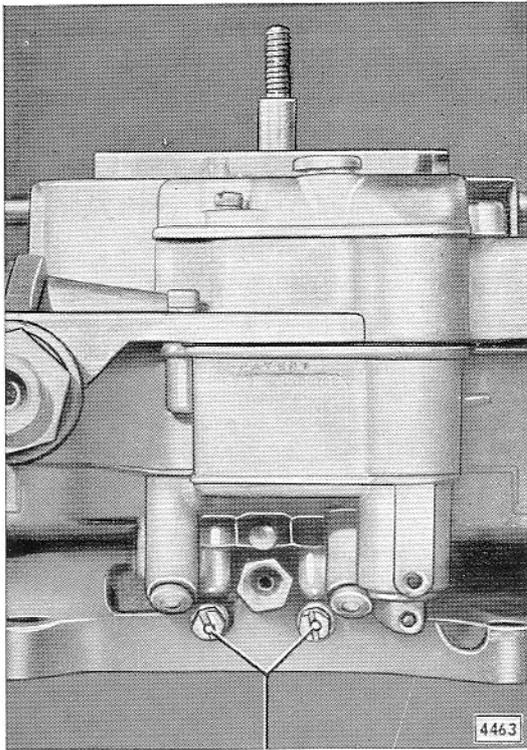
Leerlaufgemisch-Regulierschrauben handfest eingeschraubt
